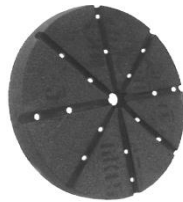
Переривчастий абразивний ріжучий інструмент
